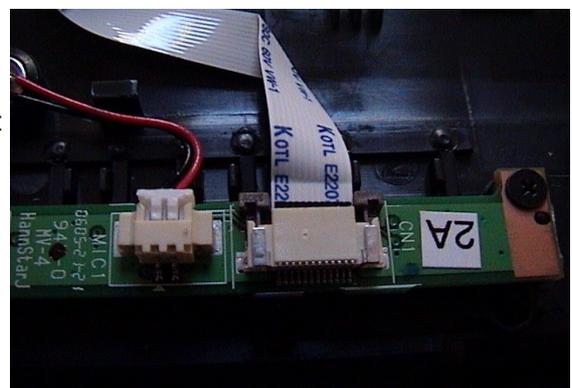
Kabel Tastenpanel, Stecker geöffnet
